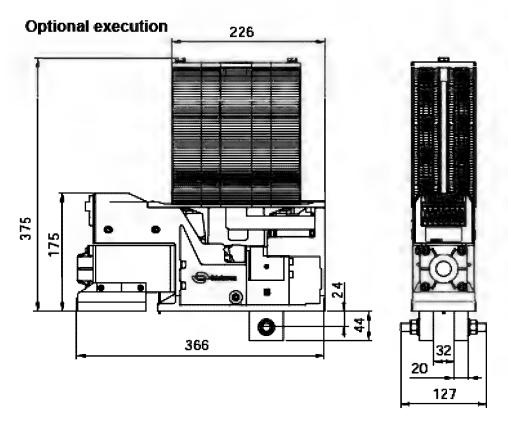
габаритный чертеж электромагнитного контактора
